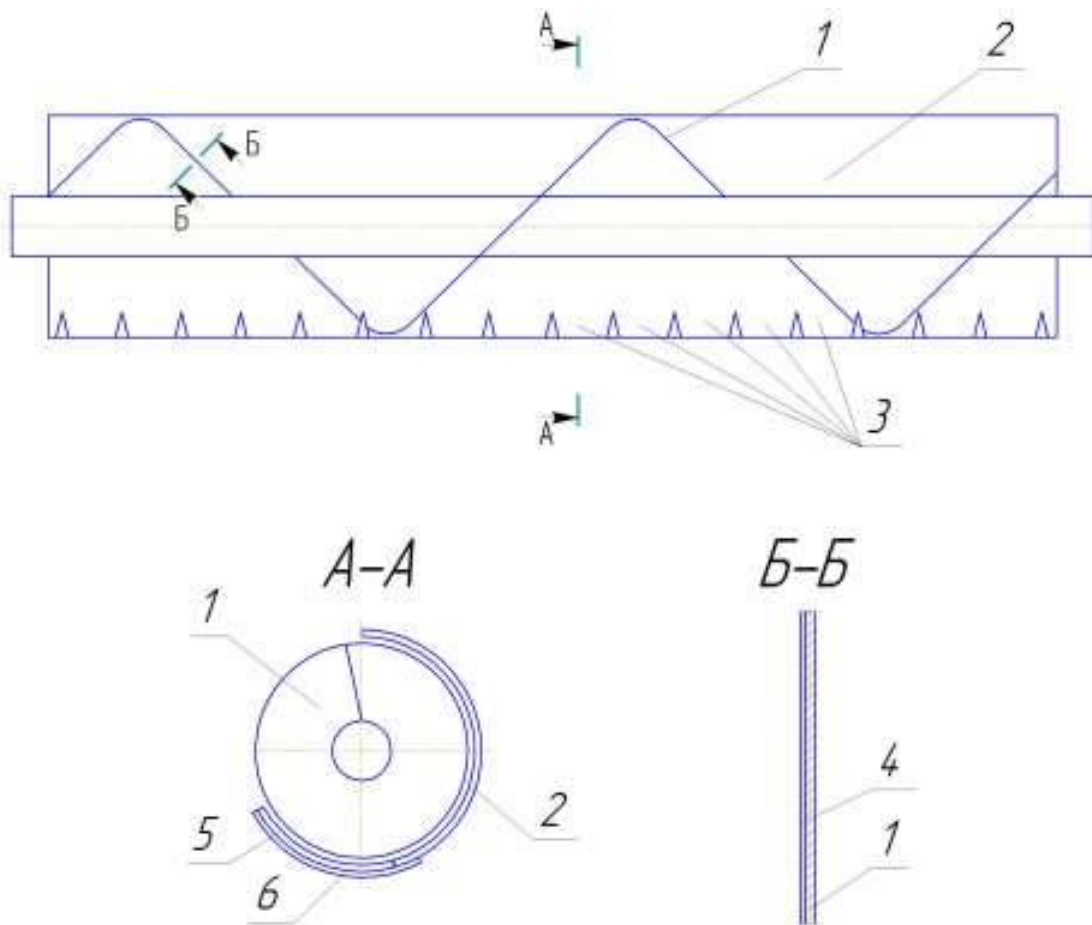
Схема шнекового ріжучого апарату з накладками із фторопласту:
